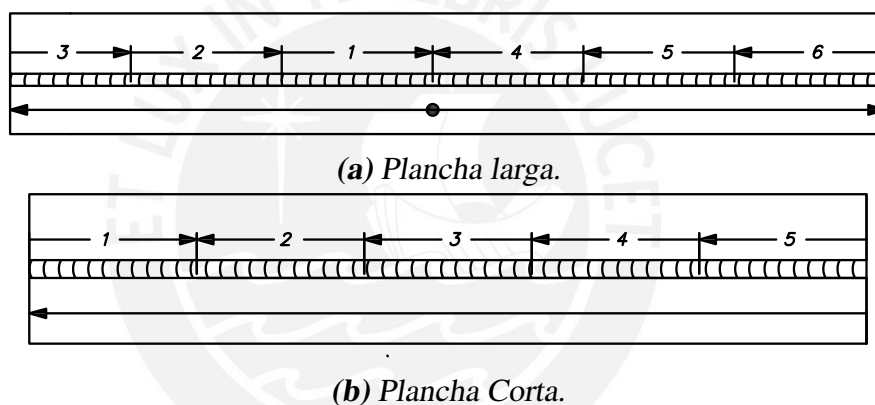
Secuencias de soldadura para planchas largas y cortas (Masubushi, 1982).
